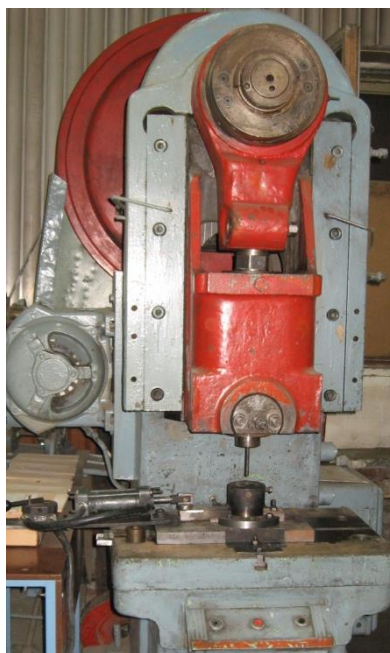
Кривошипный механический пресс К–117Д
